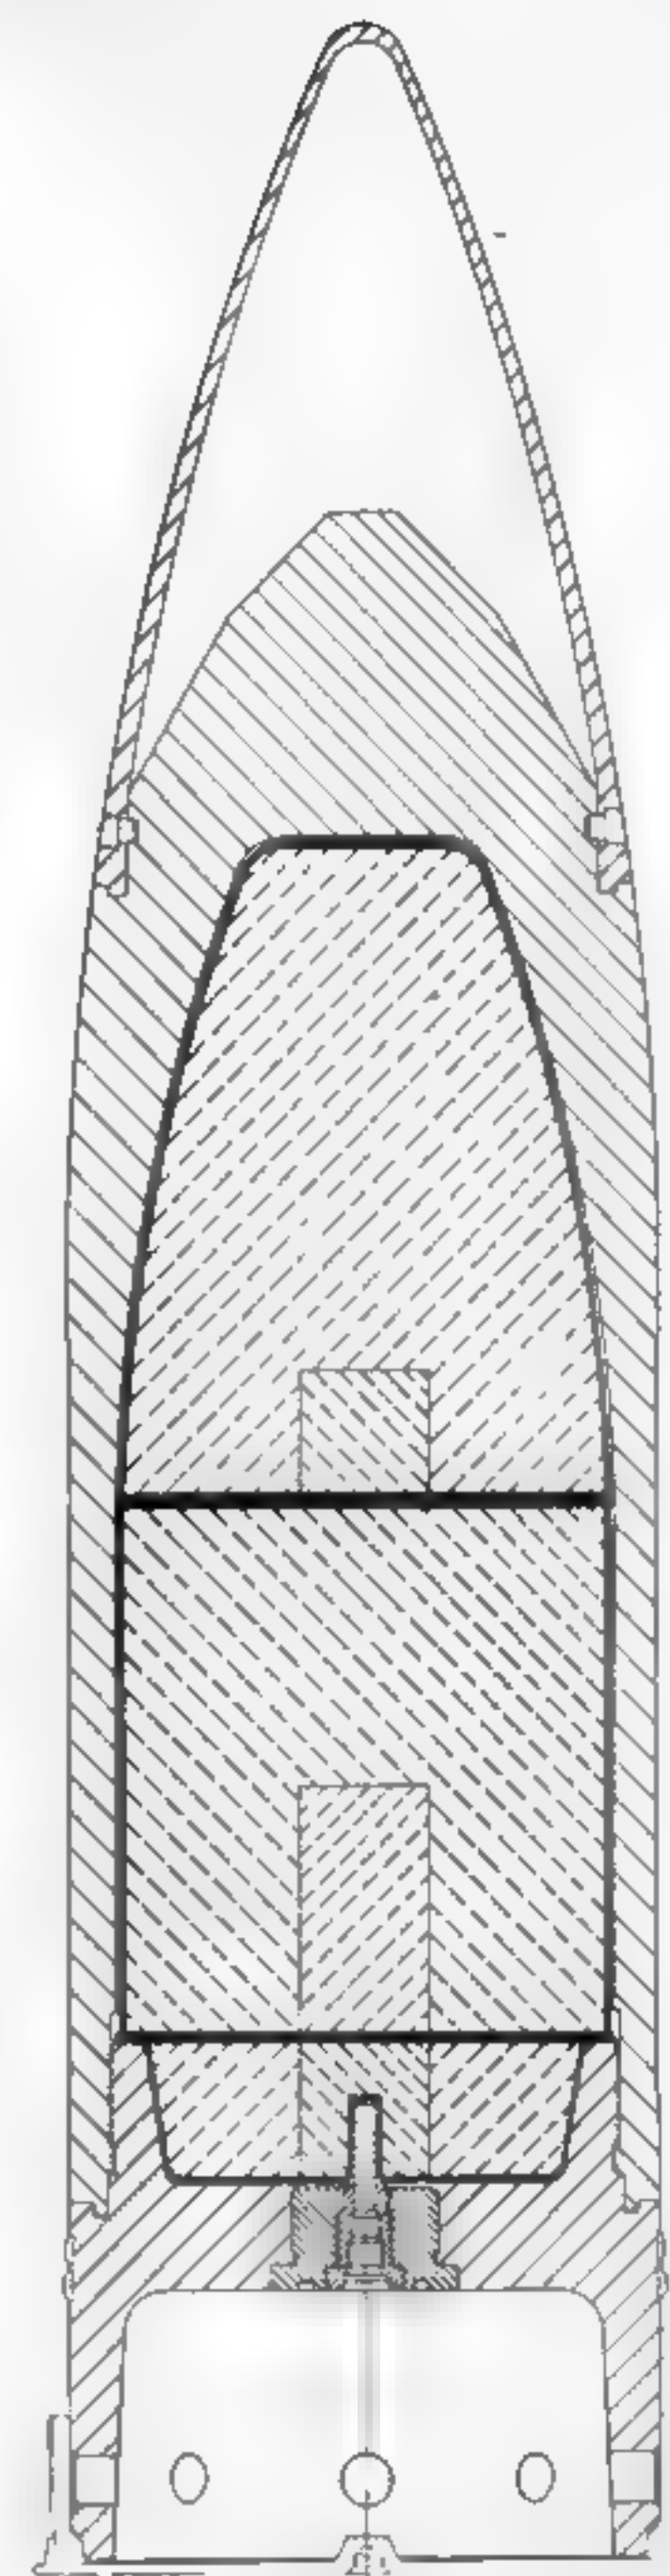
Die endgültige Form der schweren Btongranate Karl (2150 kg)
